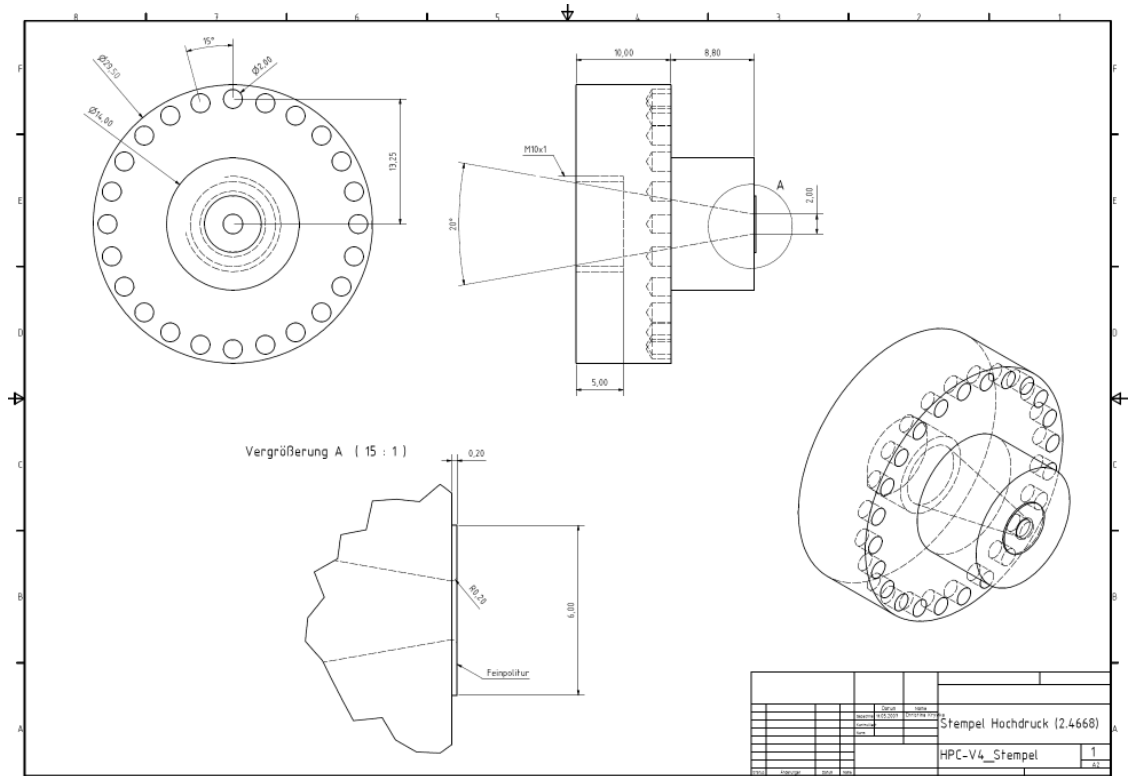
Technische Zeichnungen der Hochdruckzellenkomponenten
